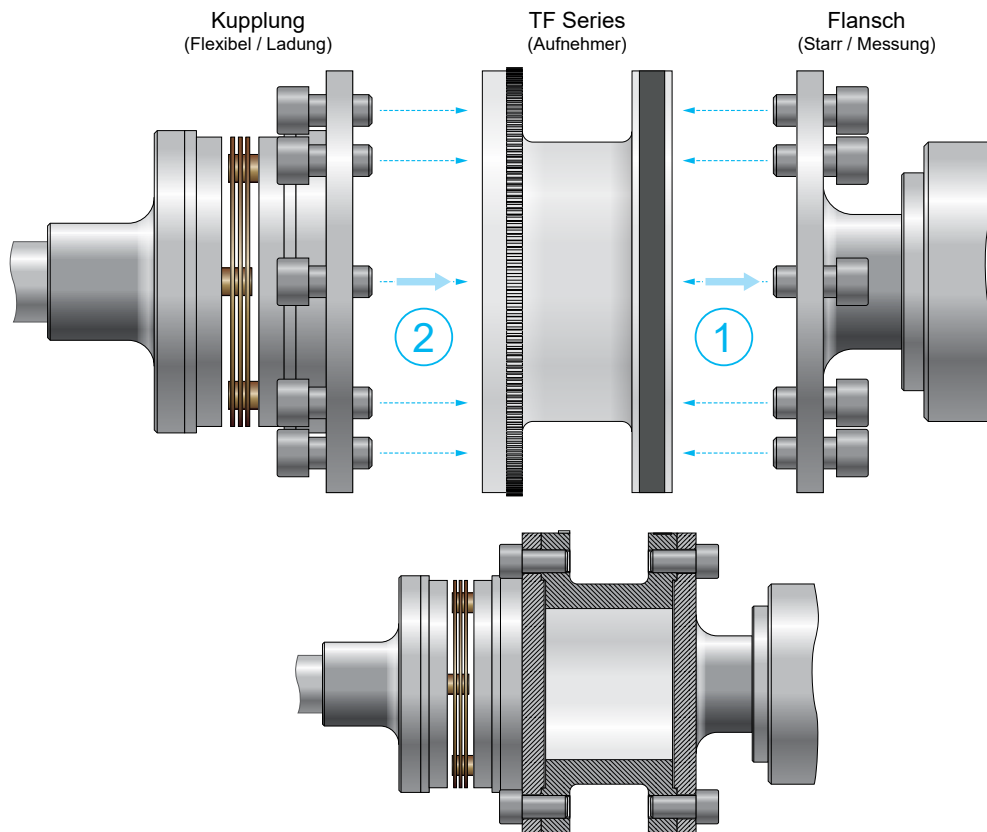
empfohlener Montageprozess für TF318 - TF320 Vertikaler Installation
